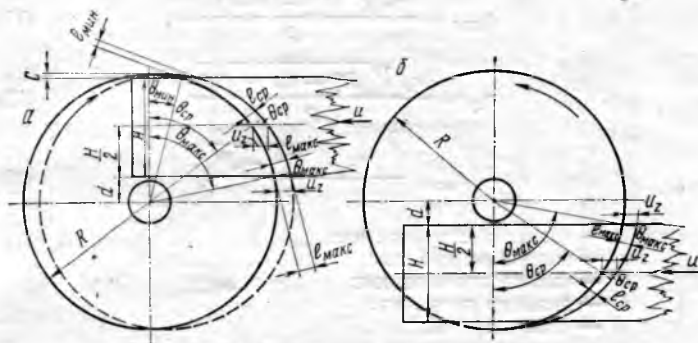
Схема образования стружки при пилении древесины круглыми пилами с расположением пильного вала: а — нижним; б — верхним
